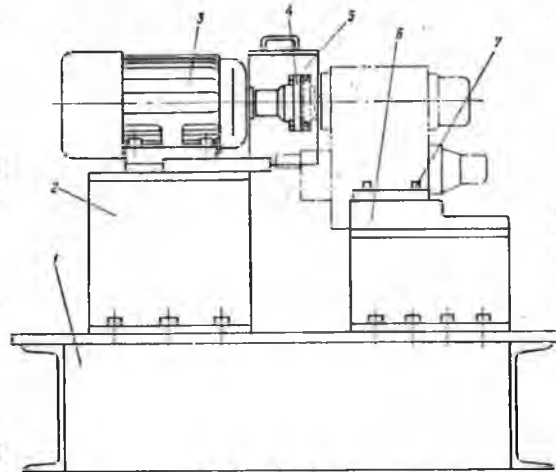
Схема стенда для обкатки редуктора ВВП.
